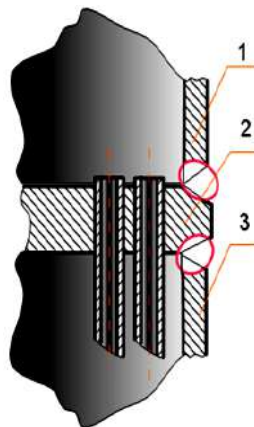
Бесфланцевый корпус с бесфланцевой решеткой
